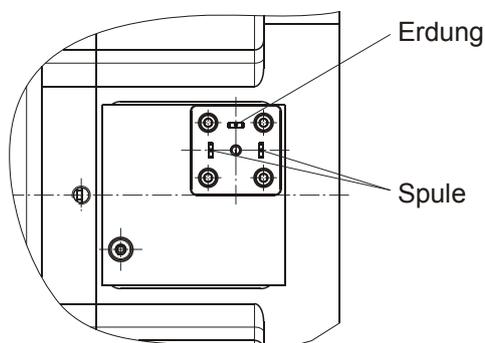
Steckerbelegung bei Ausführung mit Gerätestecker GSC 300
